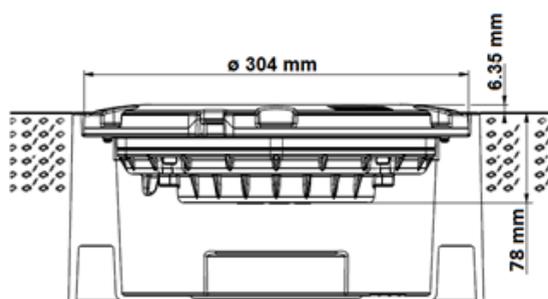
Abmessungen für 12-Zoll-Feuer
